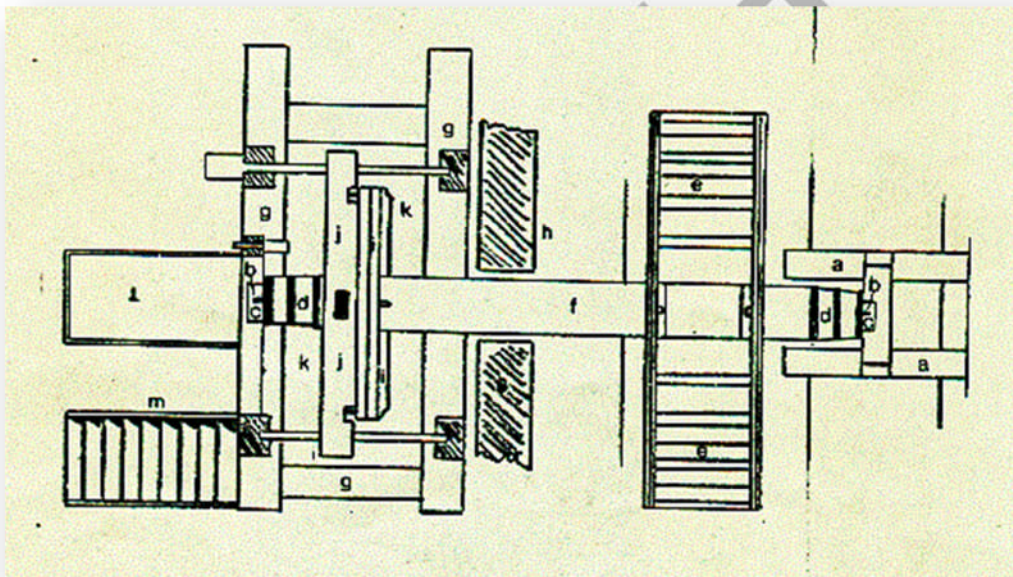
Wasserrad und Getriebe in der Draufsicht. (Zeichnung Autor)
